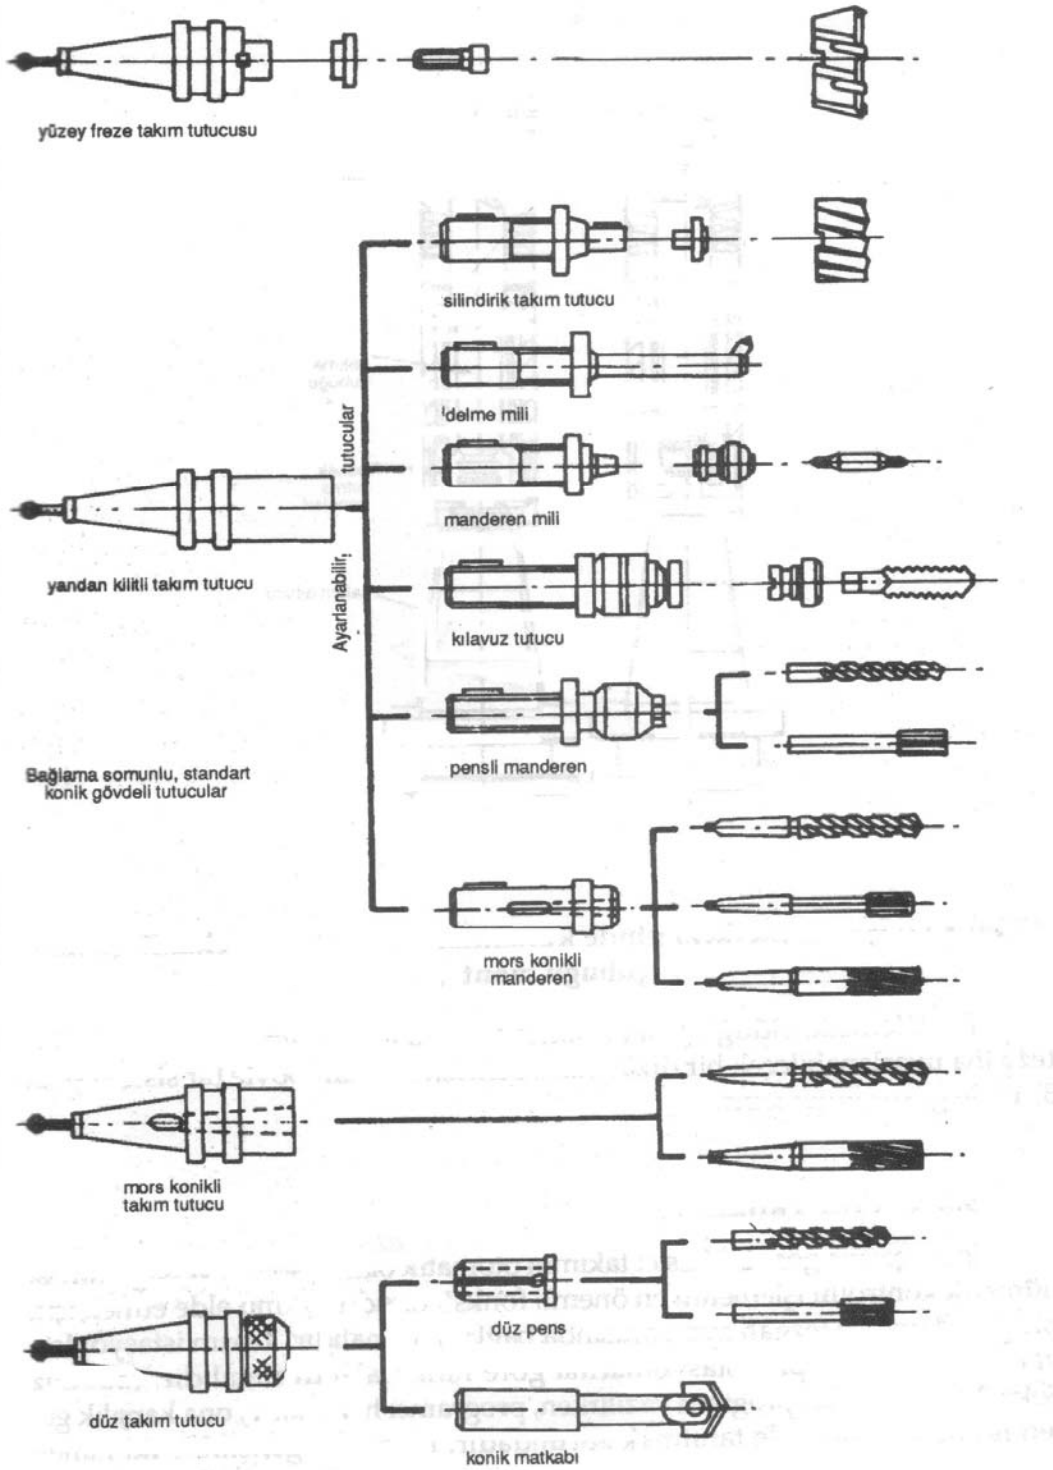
CNC tezgâhlarda kesici takım tutucuları
